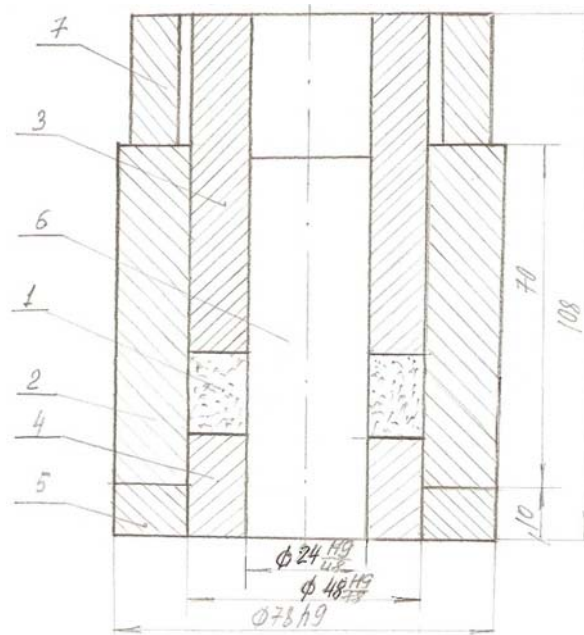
Складальне креслення прес-форми: 1 – заготовка; 2 – матриця; 3 – верхній пуансон; 4 – нижній пуансон; 5 – підкладка; 6 – голка; 7 – пресове кільце.
